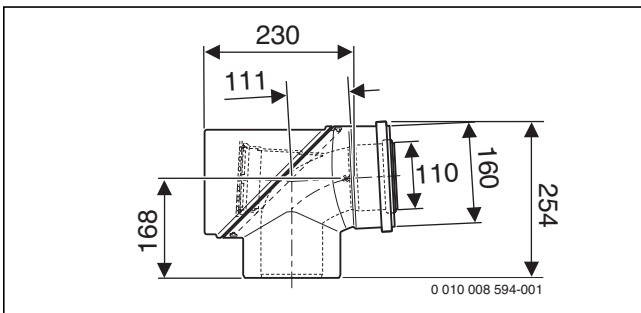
Konzentrisches T-Stück mit Prüföffnung Ø 110/160 (Maße in mm)
